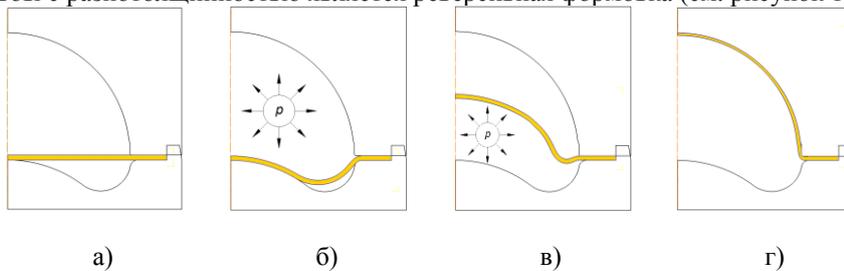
Стадии процесса реверсивной пневмотермической формовки. а) исходное состояние; б) предварительная формовка; в) окончательная формовка; г) отформованная заготовка.
